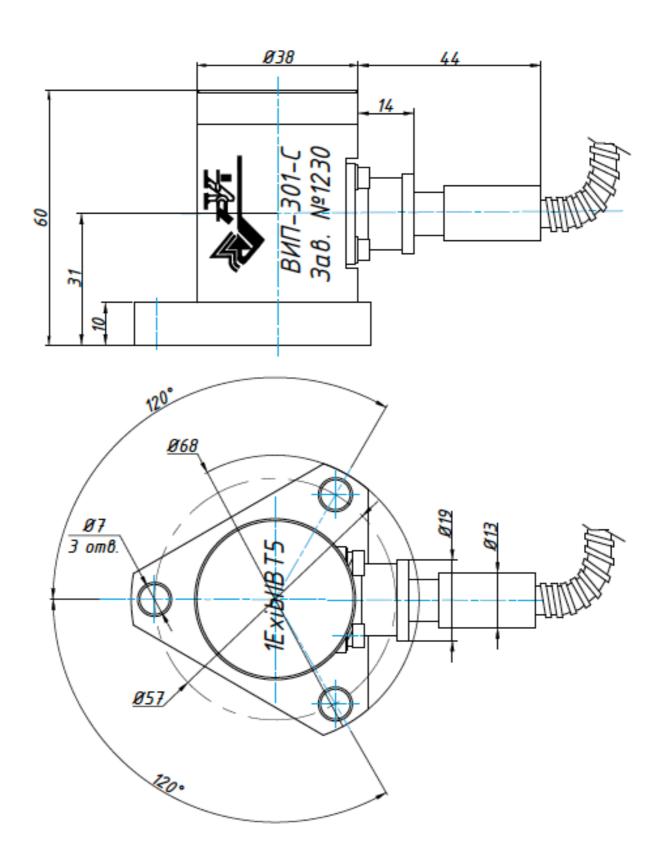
Габаритные и установочные размеры ВИП-301-С.01-3
